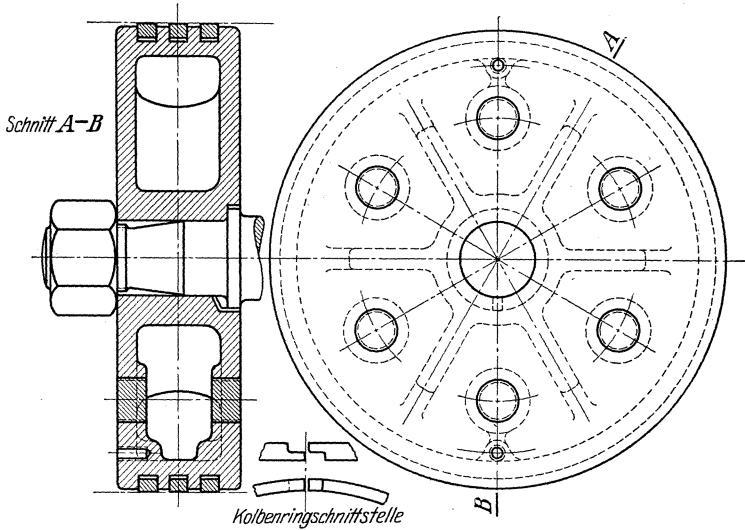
Selbsttragender Dampfmaschinenkolben.
